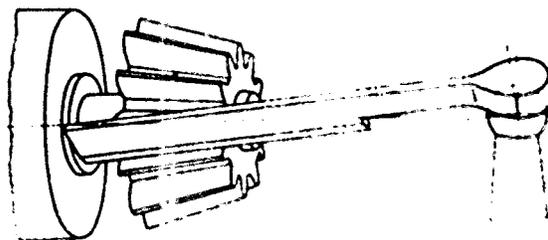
Flankenrichtungsprüfung mittels Handlinier I bei Kegelnradern
